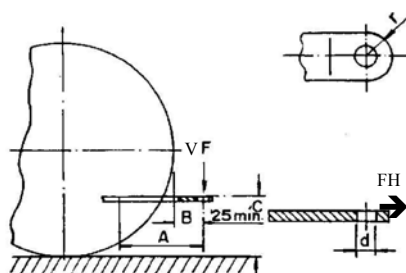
Representação das características dimensionais da barra de tração, adaptado da NBR 7811 (ABNT, 1993).
